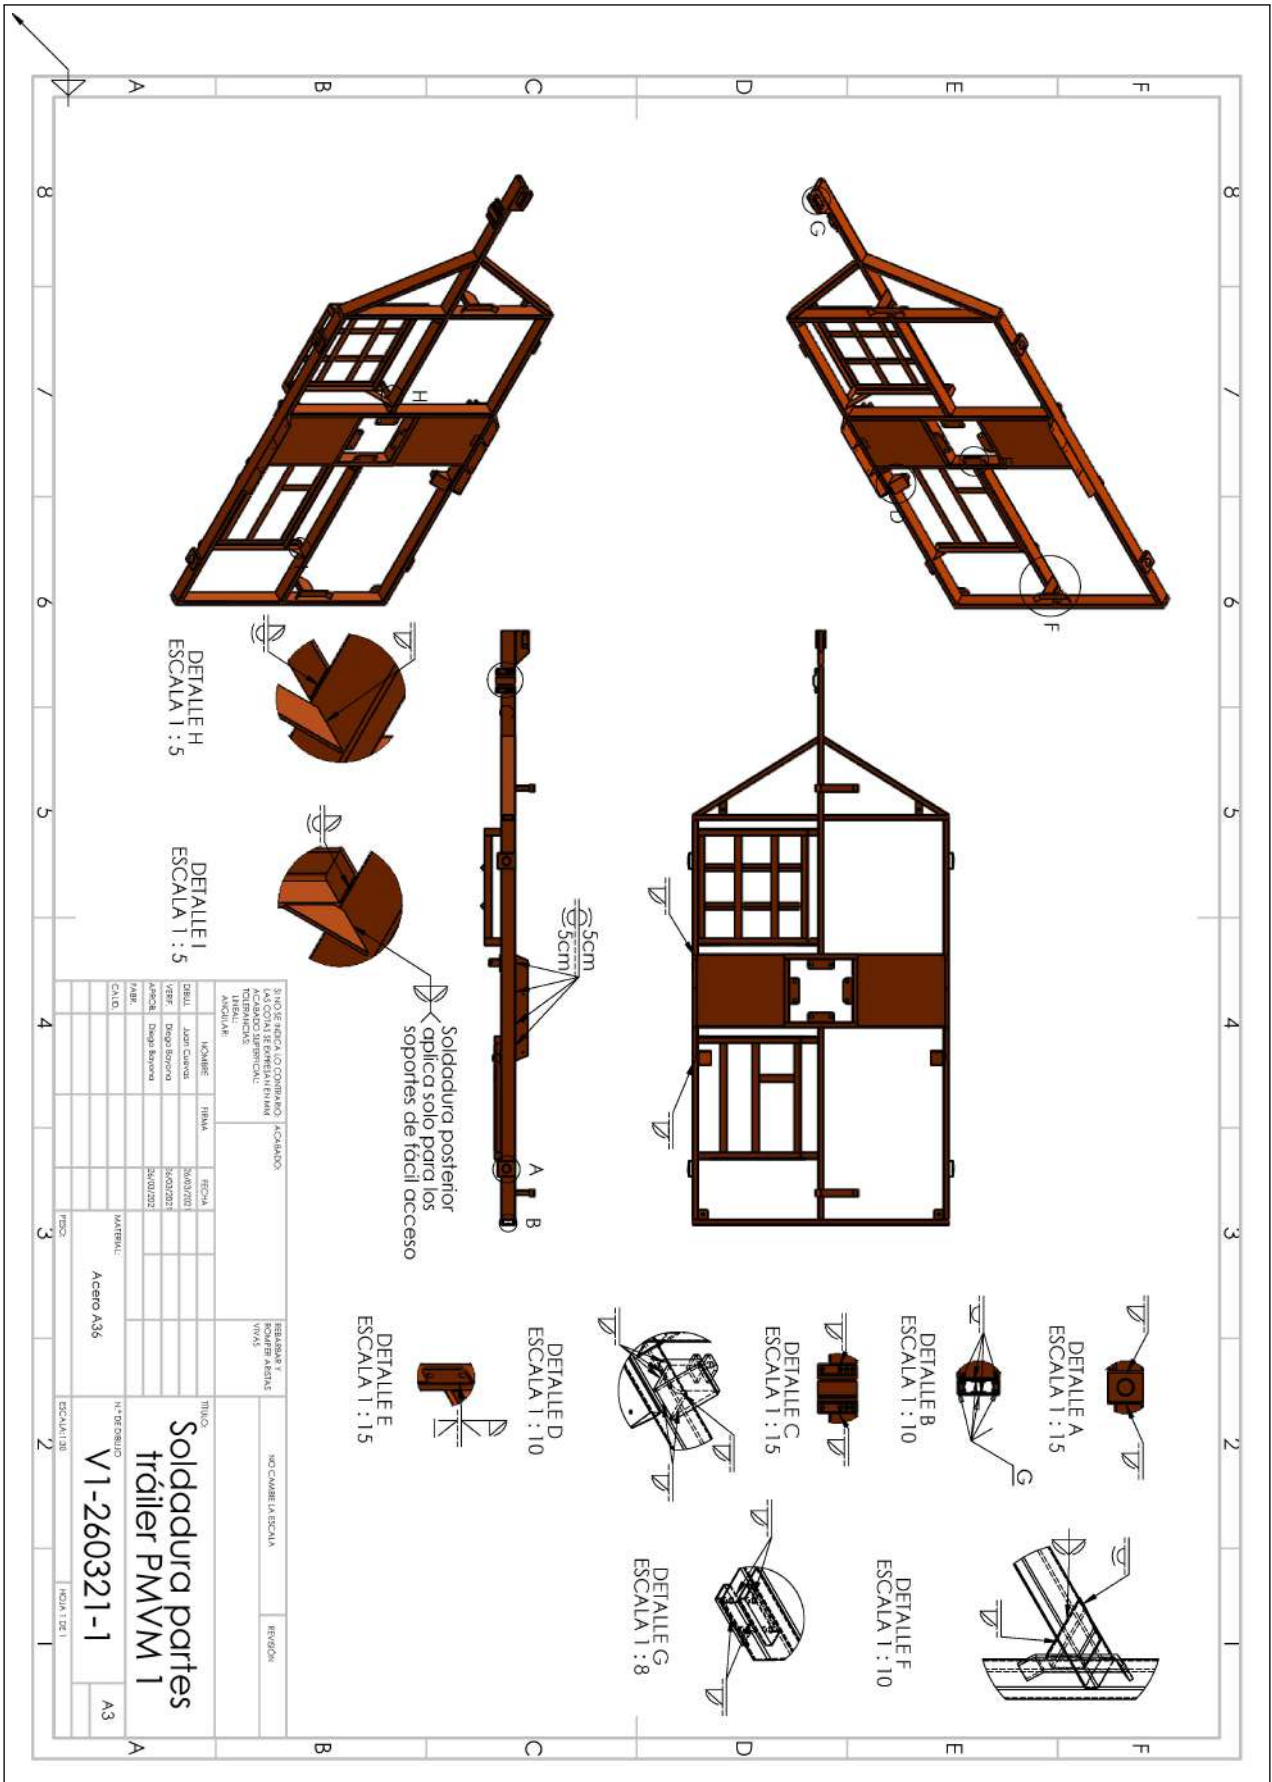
Soldadura partes tráiler PMVM 1.
